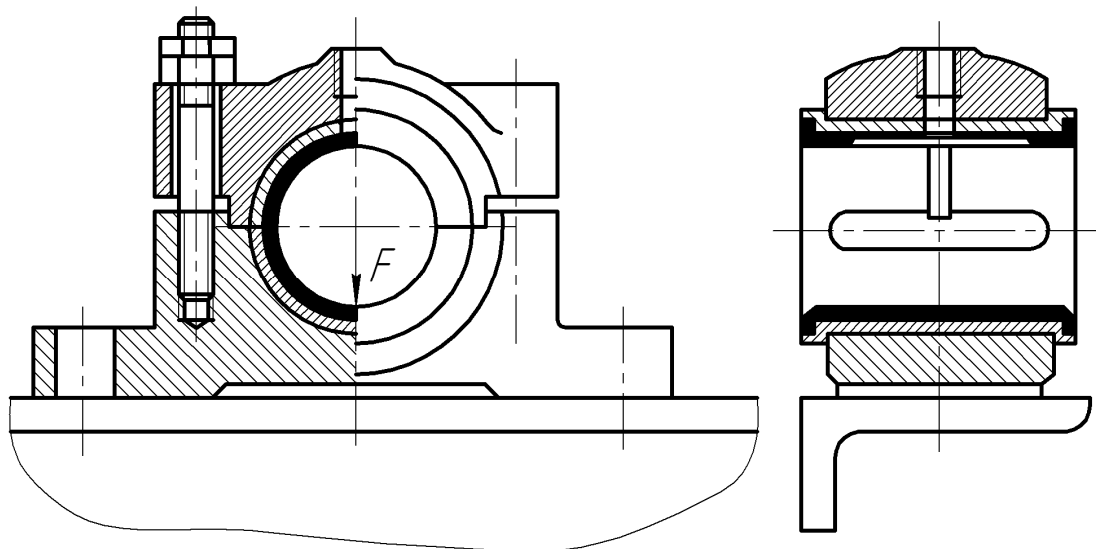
Подшипник скольжения с разъемным корпусом и вкладышем
